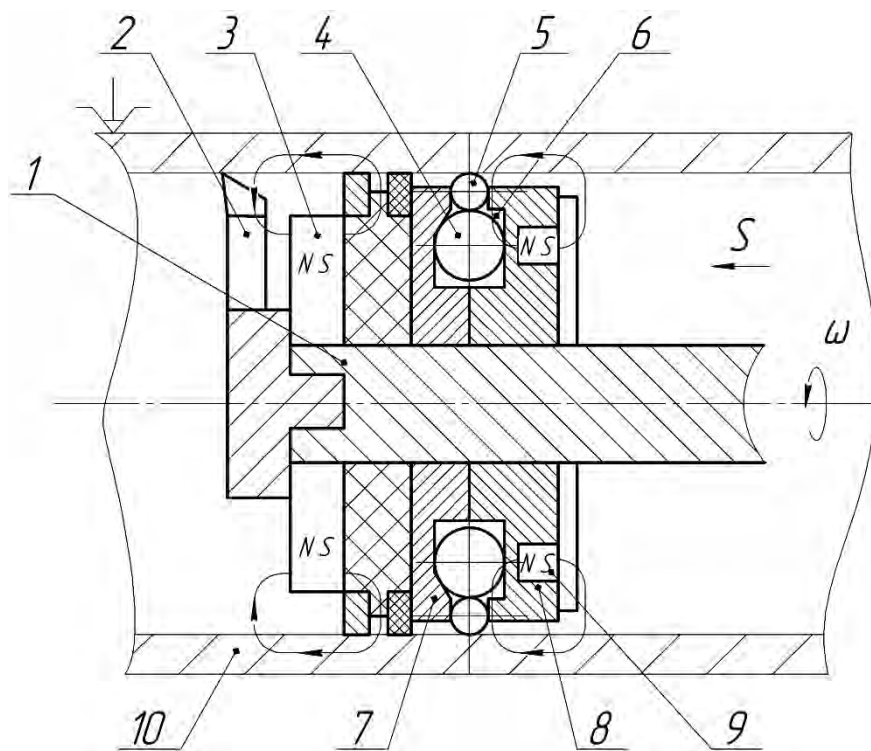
Конструкция инструмента для совмещенной обработки резанием и магнитно-динамическим раскатыванием (двухрядная компоновка)
